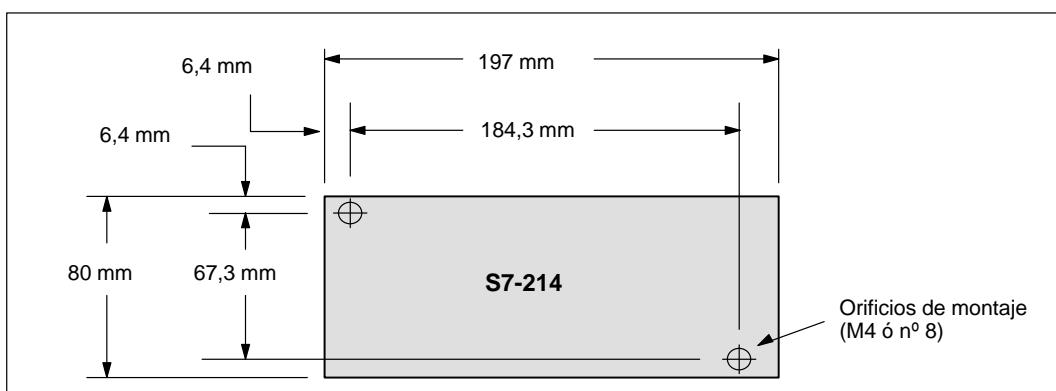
Dimensiones de montaje para una CPU S7-214
